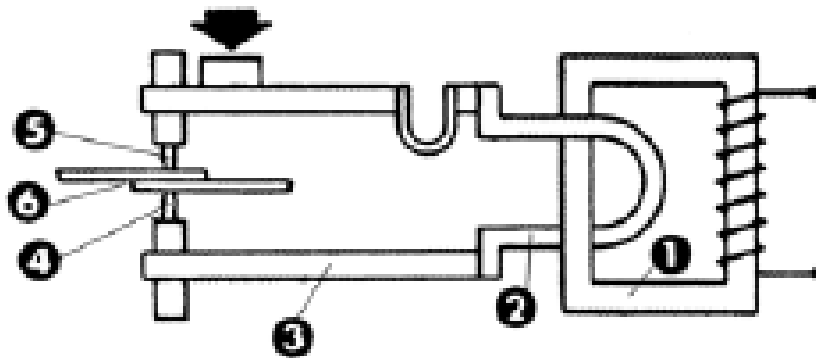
Representación esquemática de una máquina de soldar por puntos. 1) Transformación de la soldadura; 2) Secundario del transformador. 3) Circuito secundario exterior; 4) Electrodo inferior; 5) Electrodo superior; 6) Piezas superpuestas, a soldar.
